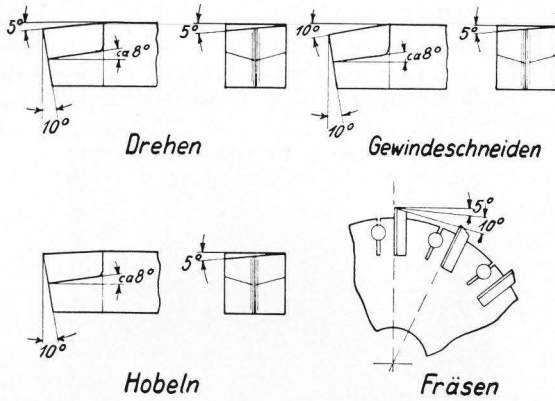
Winkelgrößen der für Glasbearbeitung bestimmte Werkzeuge.
